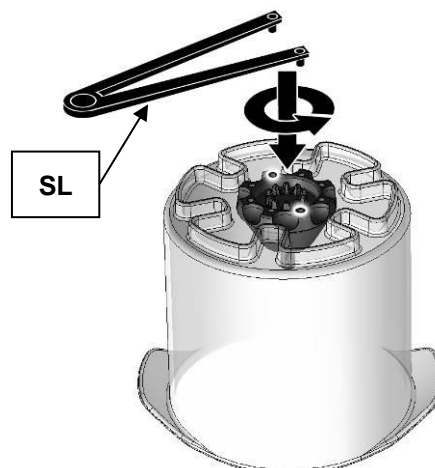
Удаление колпачка ножа с помощью торцевого штифтового гаечного ключа
